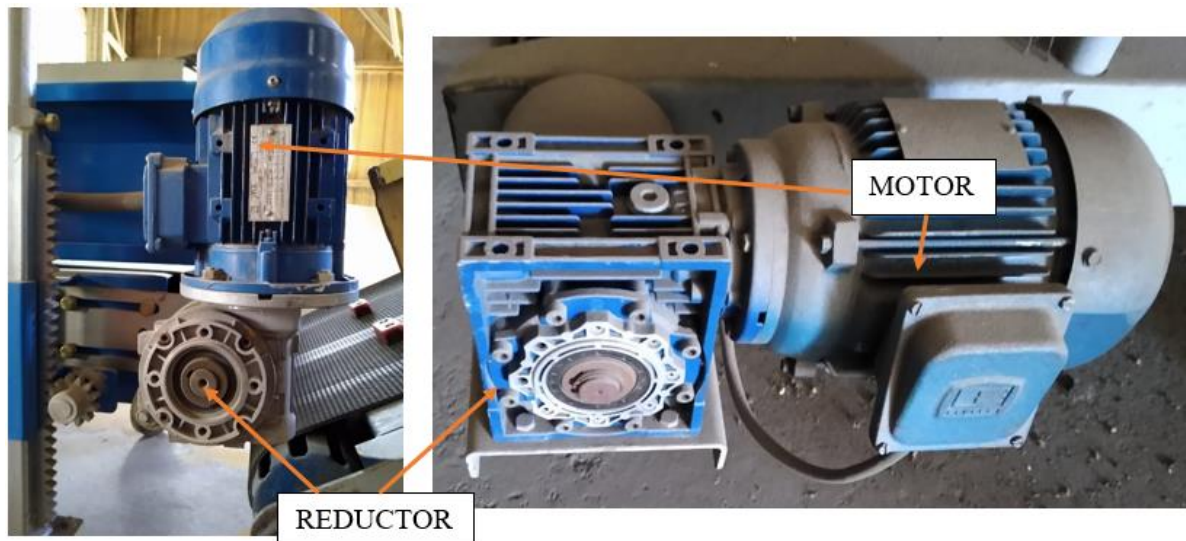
Motorreductor instalado en una cinta transportadora.
